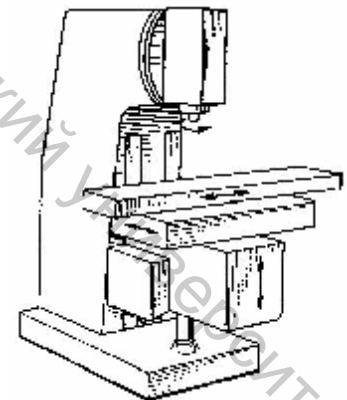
Компоновка консольного вертикально-фрезерного станка
